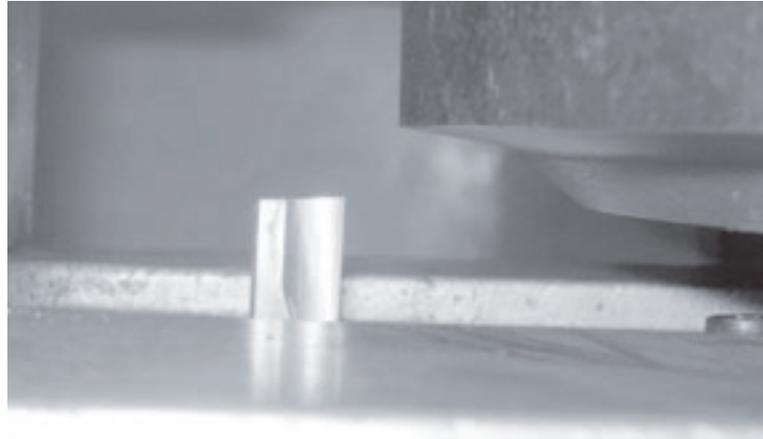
Entfernen Sie die Abdeckung des Werkzeughalters und führen Sie den Werkzeughalter in den Werkzeugschlitten ein.
